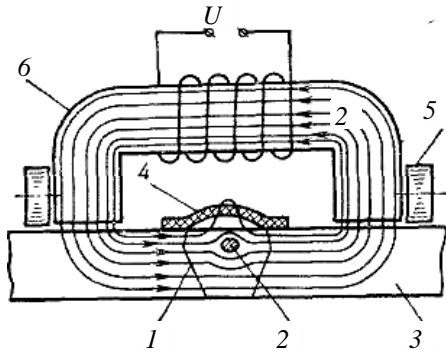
Схема намагнічування зварного шва разом з магнітною стрічкою:
